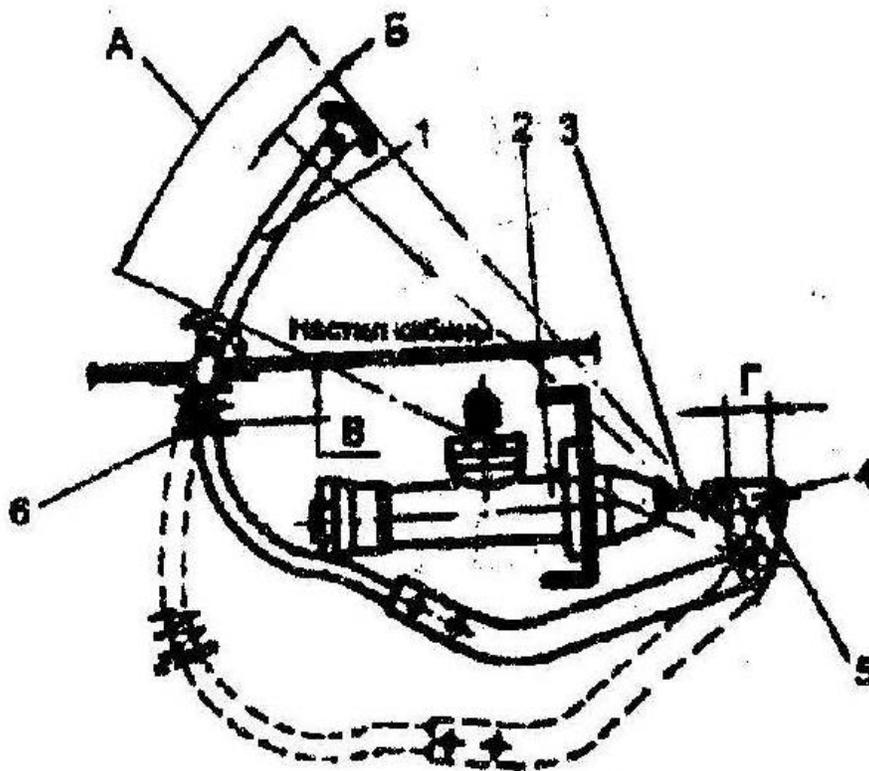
Регулировка толкателя главного гидроцилиндра системы управления муфтой сцепления:
